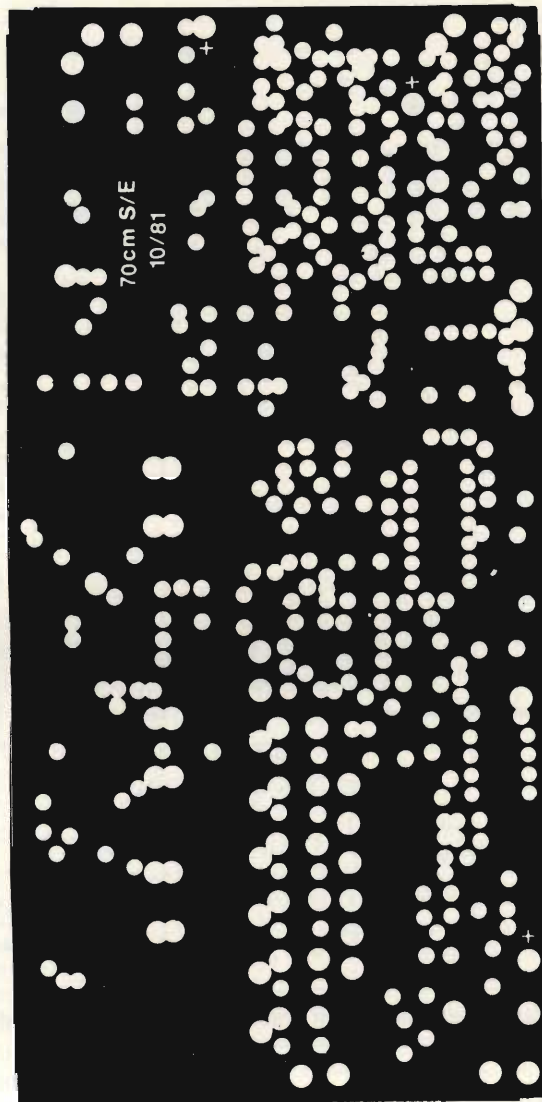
Il lato componenti del circuito stampato verrà inciso secondo questa matrice.
